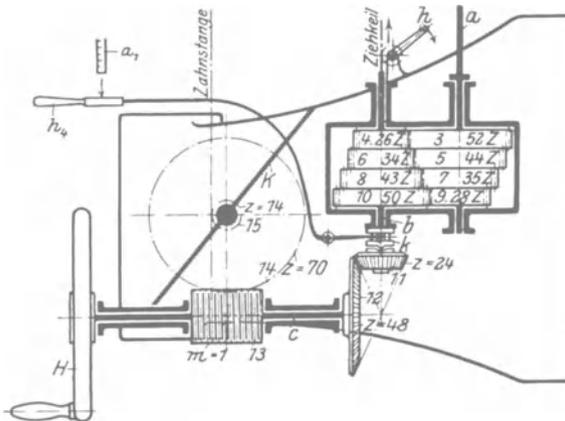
Steuerung einer Bohrmaschine. (Zahnrad 15 hat $m = 3$.)
